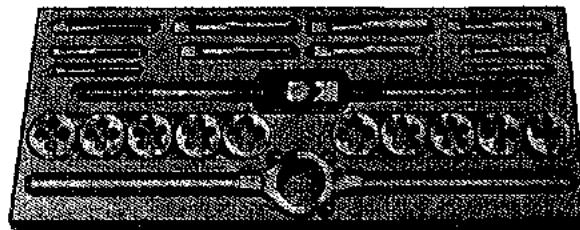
Juego de herramientas para roscar (Morse Twist Drill & Machine Co.)
